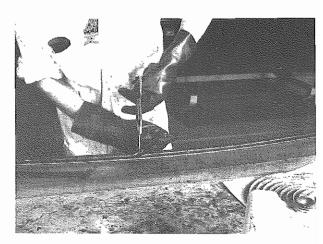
Liberare i terminali cavi di riscaldamento Free heating cables terminals
